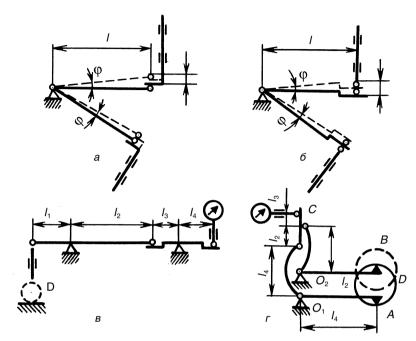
Схемы рычажных передач: а — синусный рычаг; б — тангенсный рычаг; в — двухрычажная схема; г — трёхрычажная схема
